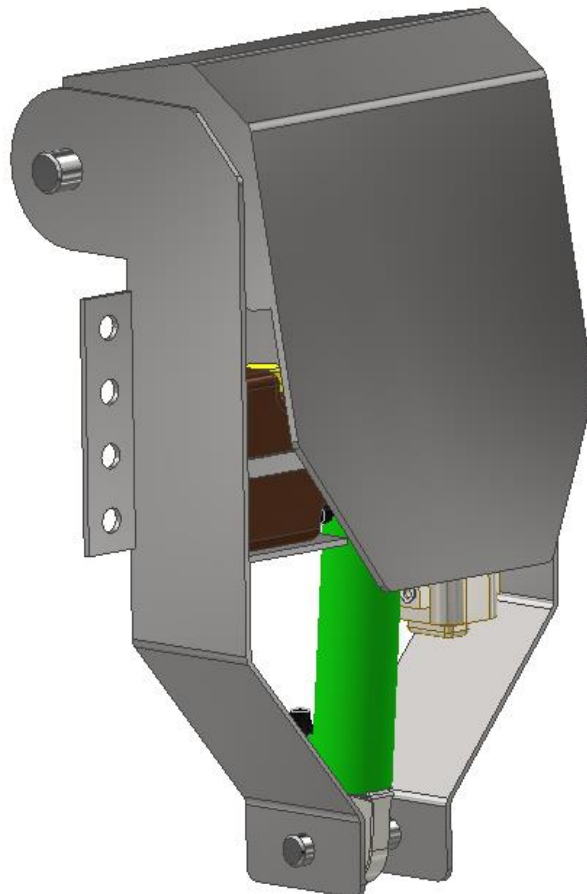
Schématické vyobrazení lodního motoru ve vyklopené poloze
